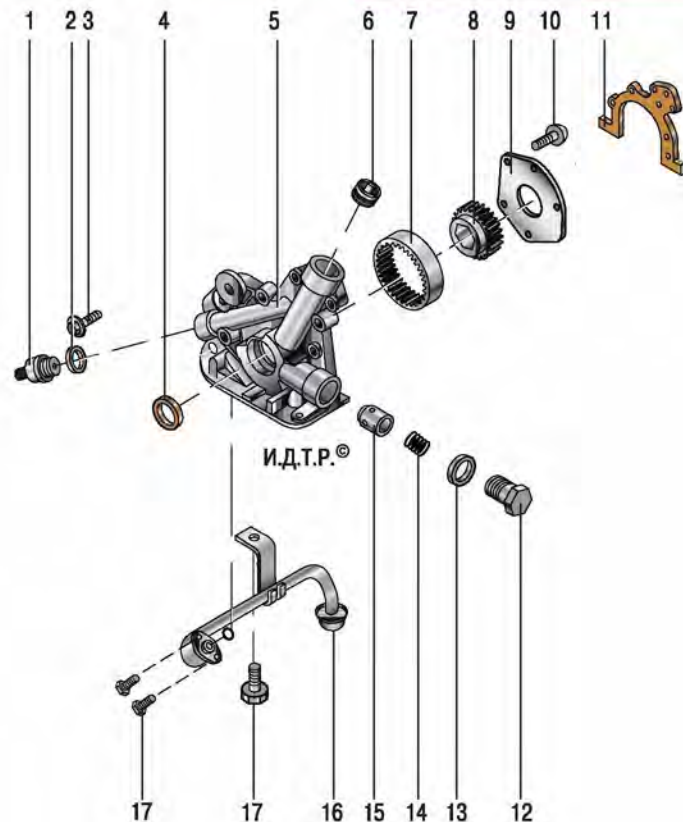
Детали масляного насоса: 1 – датчик аварийного падения давления масла; 2 – прокладка датчика аварийного падения давления масла; 3 – болт крепления масляного насоса; 4 – передний сальник коленчатого вала; 5 – корпус насоса; 6 – предохранительный клапан; 7 – ведомая шестерня; 8 – ведущая шестерня; 9 – крышка корпуса; 10 – винт крепления крышки; 11 – прокладка корпуса; 12 – пробка редукционного клапана; 13 – пружина редукционного клапана; 14 – пружина редукционного клапана; 15 – плунжер; 16 – маслоприемник; 17 – болт крепления маслоприемника
